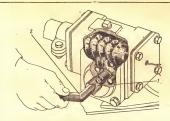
Регулировка зацепления ролика с червяком автомобиля УАЗ-69: ι — регулировочный винг; ι — ключ.
